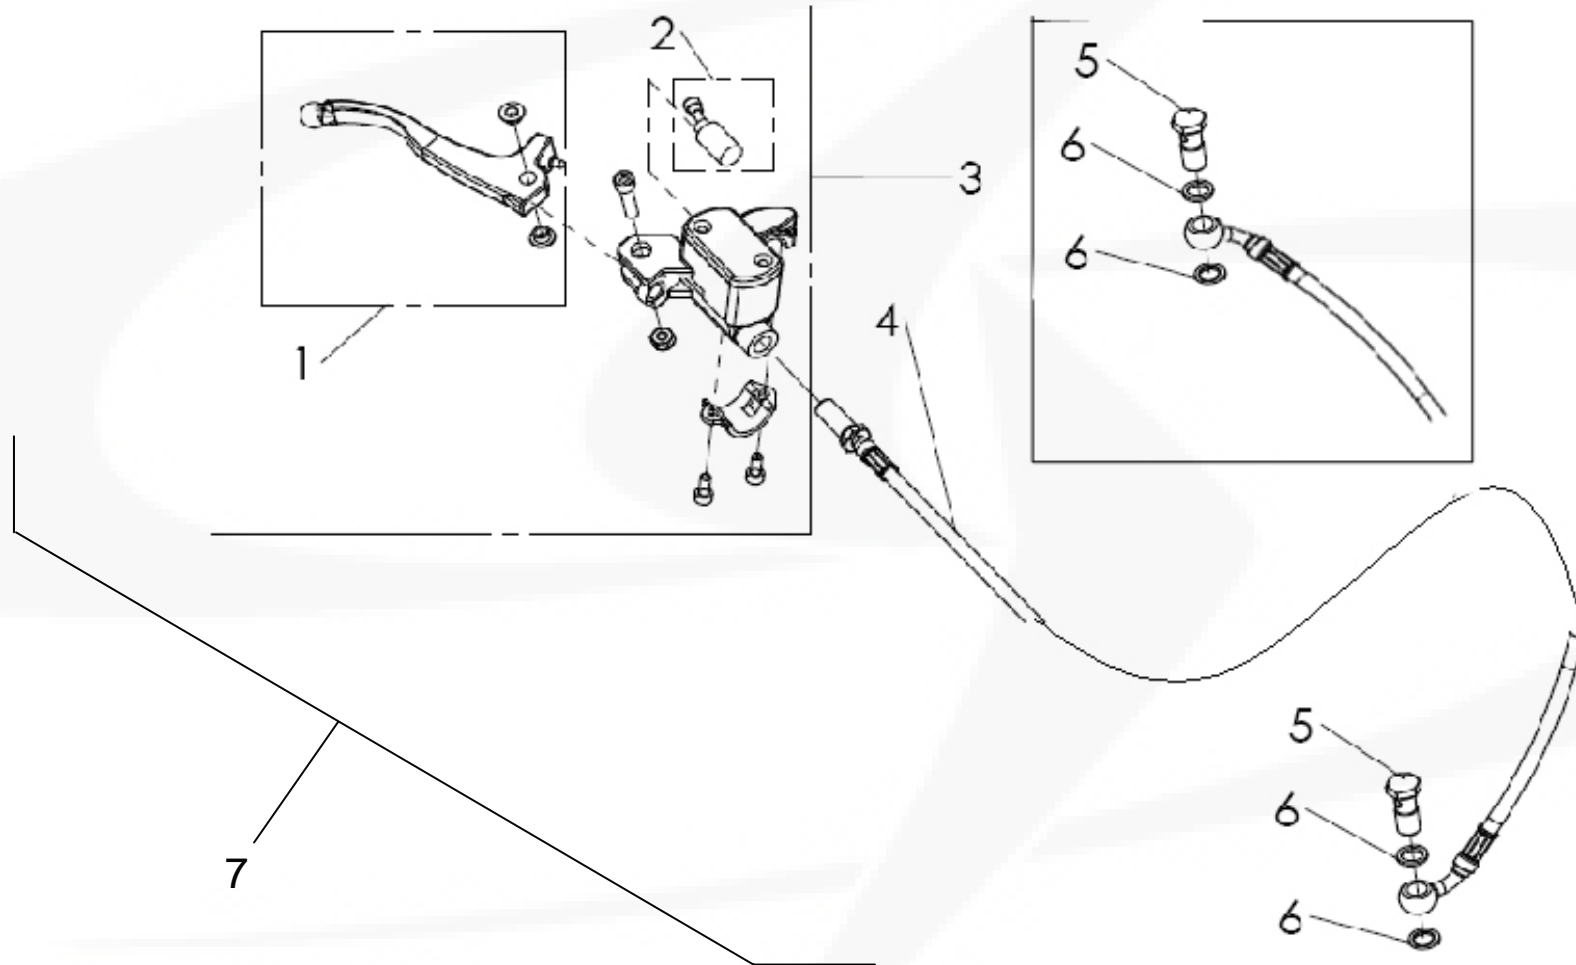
MAÎTRE CYLINDRE FREIN AVANT / FRONT BRAKE MASTER CYLINDER / BOMBA FRENO DELANTERO
